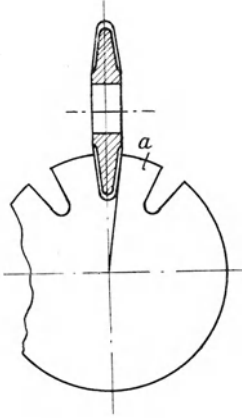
Das Fräsen der Nuten für hinterdrehte Fräser.
